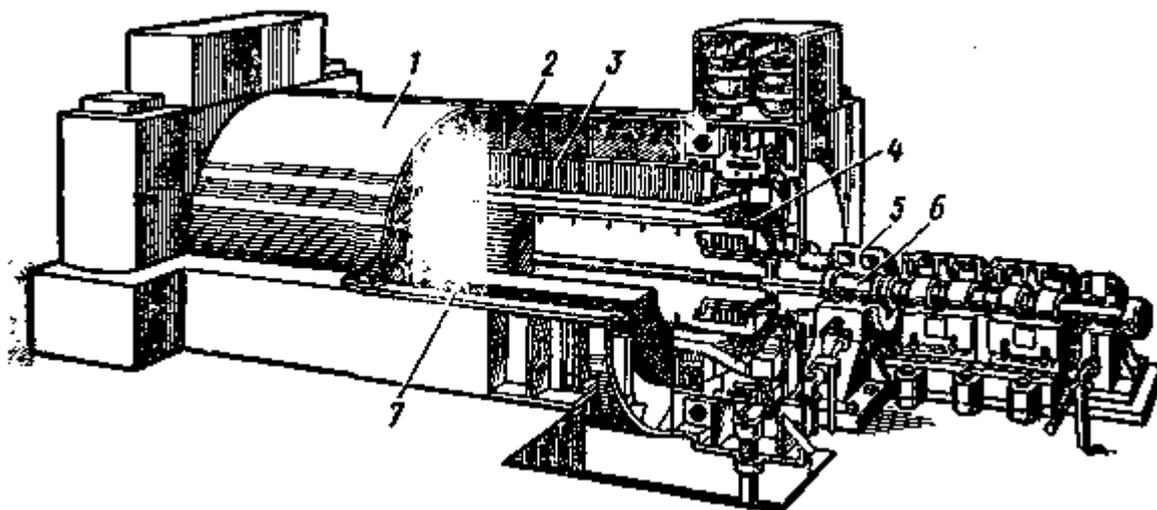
Общий вид турбогенератора ТВВ-1200-2: 1 – корпус; 2 – камеры для сбора и распределения охлаждающего газа; 3 – статор; 4 – обмотка статора; 5 – подшипник; 6 – вал; 7 – ротор
